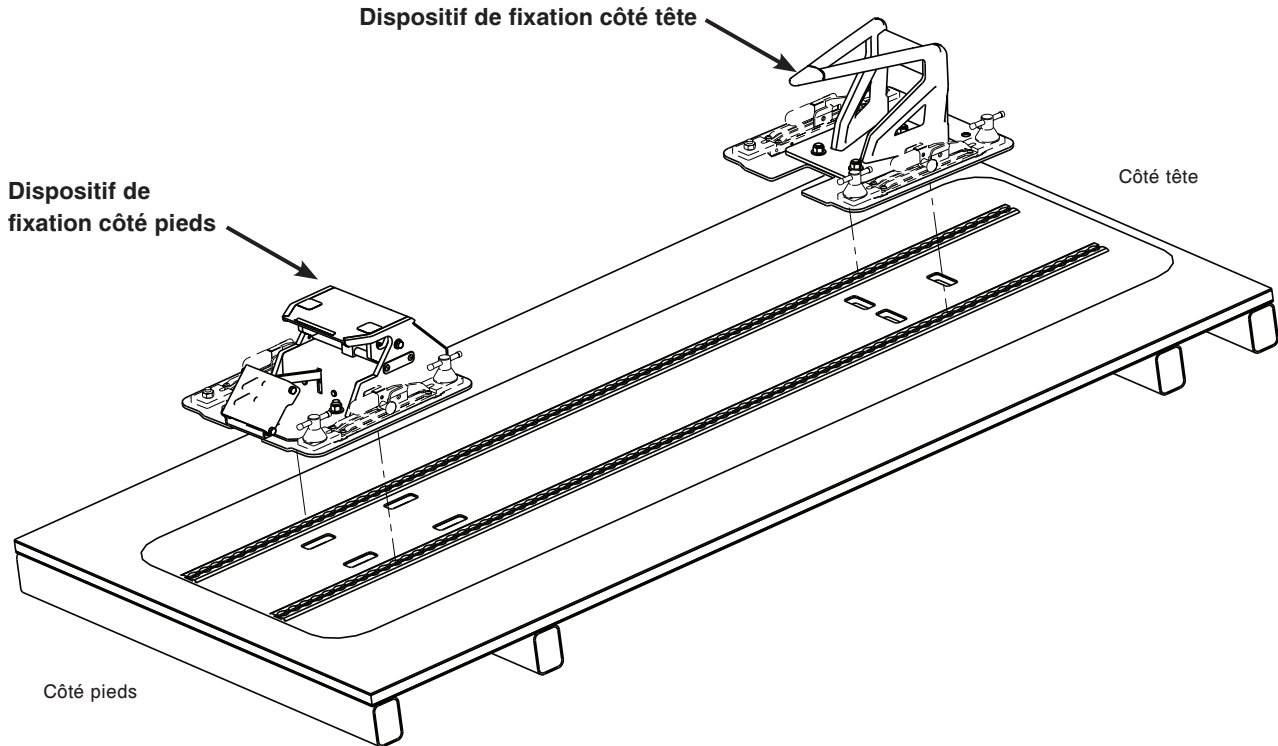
Dispositif de fixation côté tête et côté pieds – installation des rails de plancher
